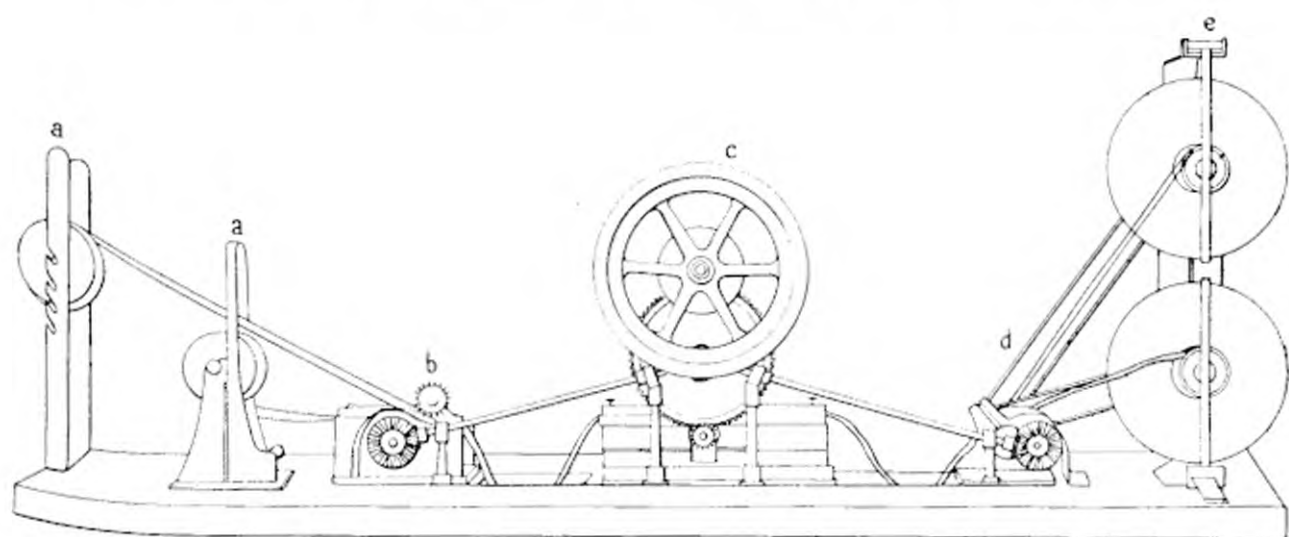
Perforeuse Lux, vue à l'arrière.
